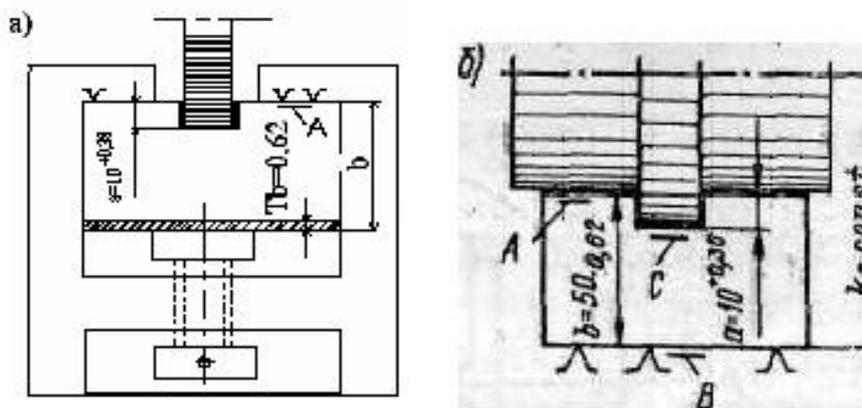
Фрезерование паза от технологической базы А, совпадающей с конструкторской
